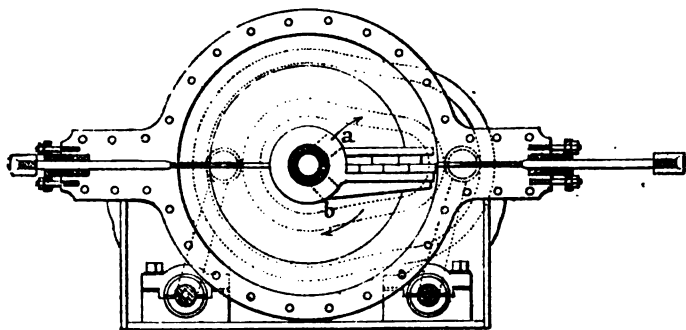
Machine rotative Pecqueur (coupe transversale).
